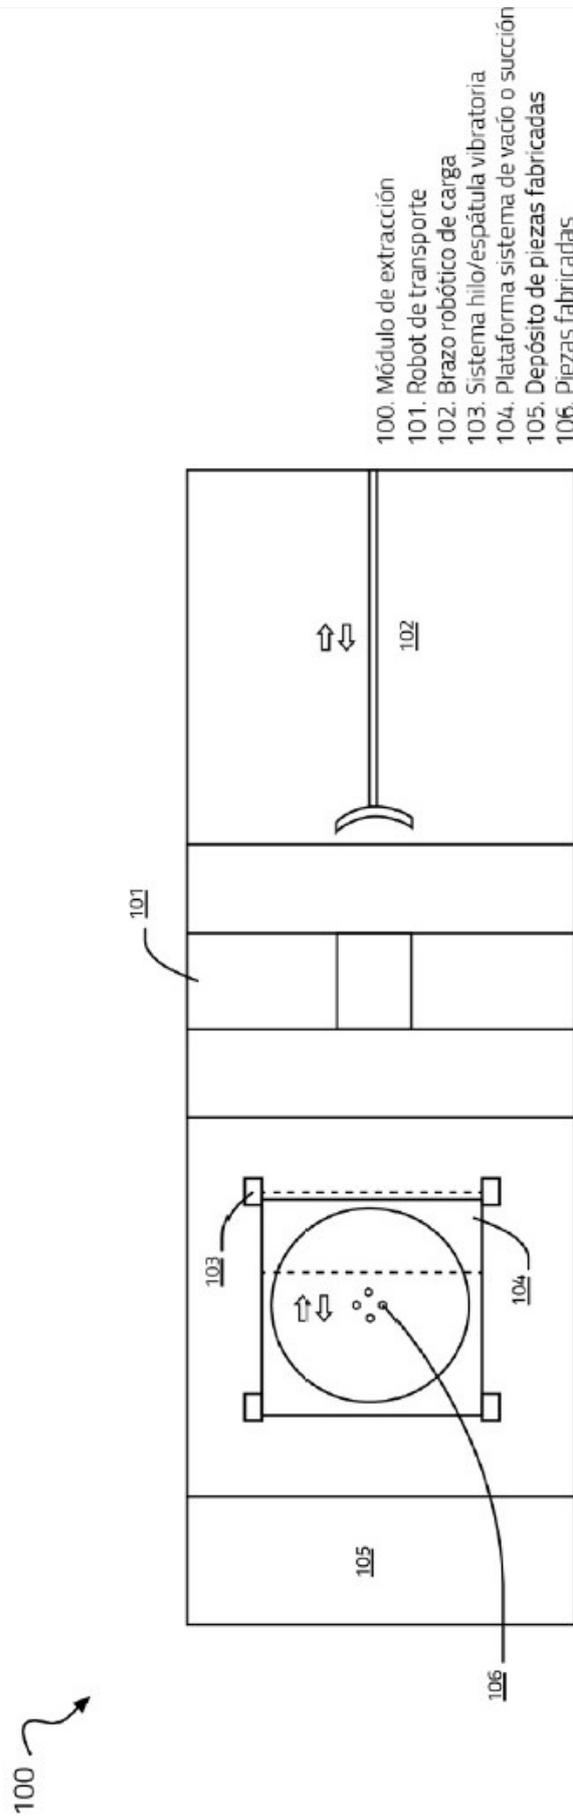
B.- Detalle en planta de un módulo de extracción de piezas fabricadas
